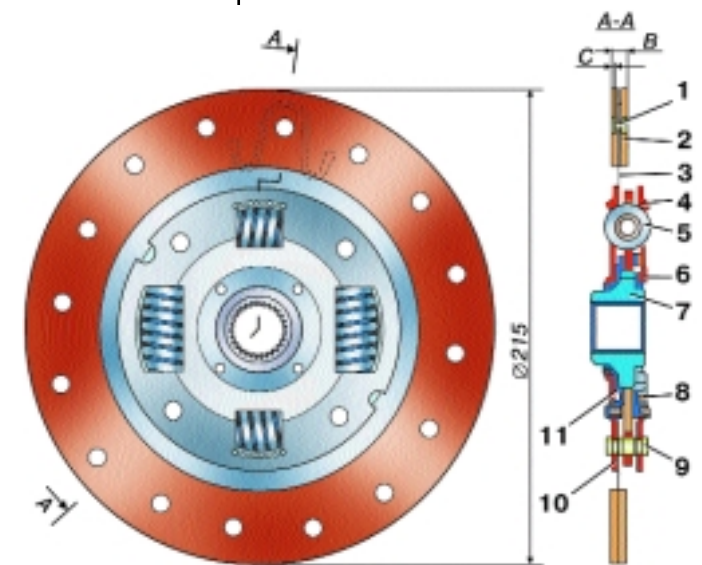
Ведомый диск сцепления «Валео» в сборе: 1 – заклепка крепления фрикционных накладок; 2 – фрикционная накладка; 3 – пружинная пластина; 4 – пластина демпфера; 5 – пружинная пластина; 6 – упорное кольцо демпфера; 7 – ступица ведомого диска; 8, 11 – фрикционные кольца; 9 – упорный палец; 10 – ведомый диск; В – размер (6,8±0,2) мм под нагрузкой 458,7 кгс; С – размер не менее 1,3 мм
